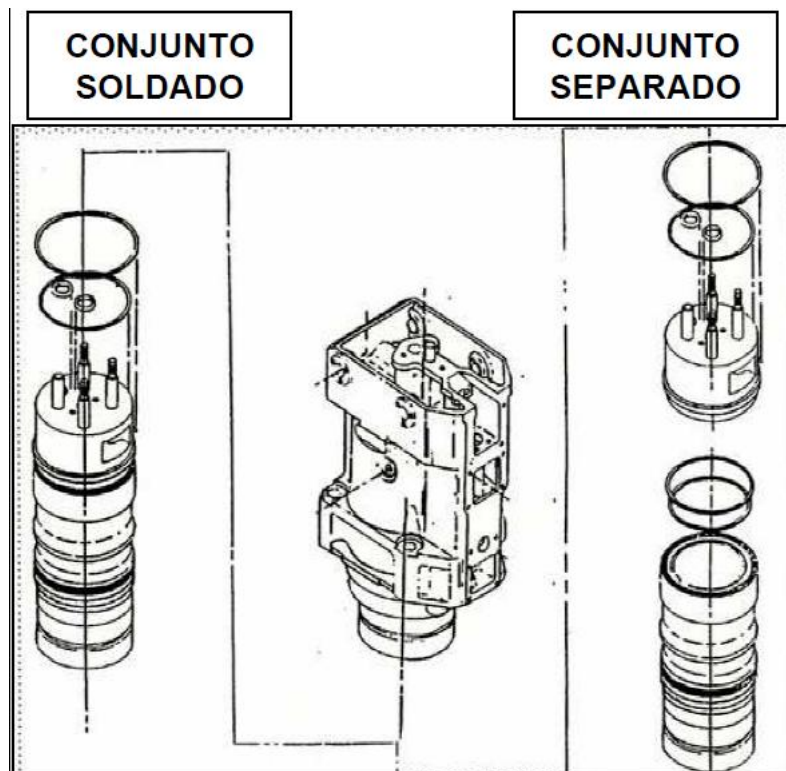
Conjuntos de força do motor diesel conjugado (soldado) e separado.
